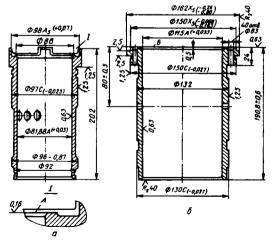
Гильзы компрессоров: а — прямоточного компрессора АУ-45; б — непрямоточного компрессора П110
